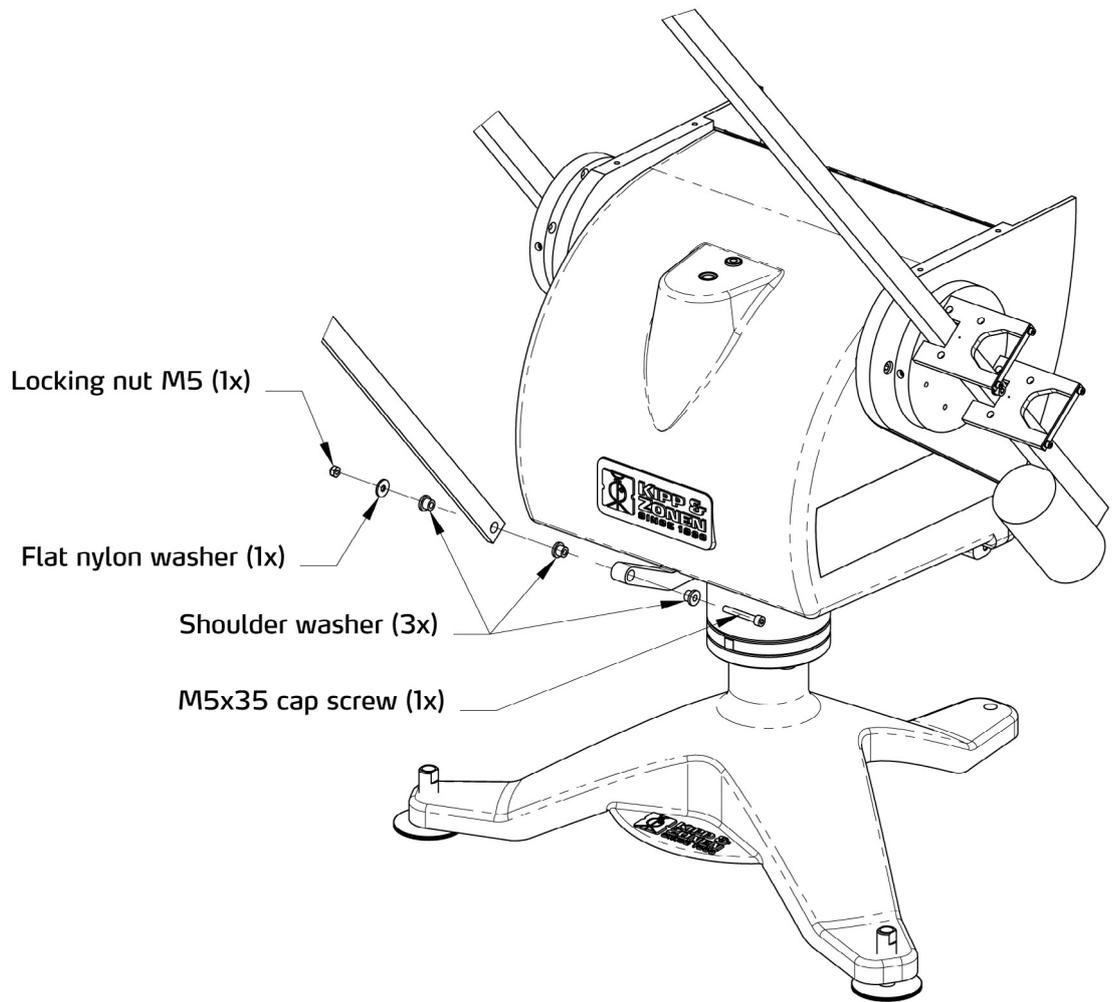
Montaje de la pieza inferior del brazo de plato de sombra
